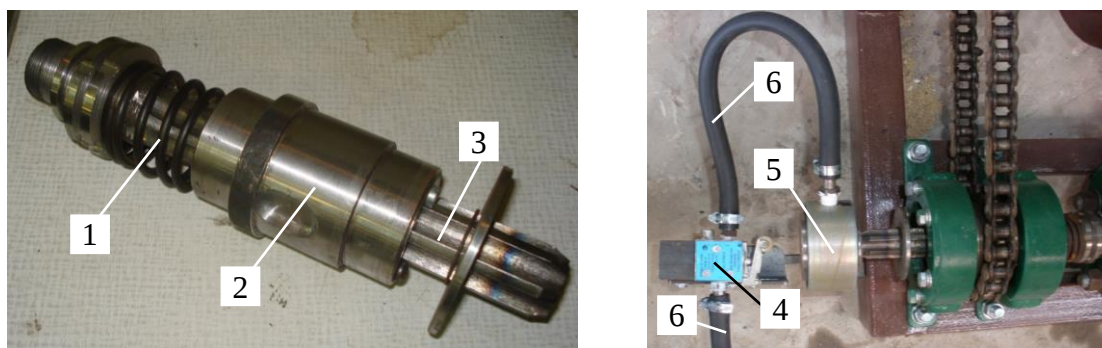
Механізм увімкнення пневморозподільника: 1 – пружина стиснення; 2 – корпус; 3 – шліцьовий вал з напівкруглими канавками; 4 – пневморозподільник; 5 – обертовий пневмоперехід
